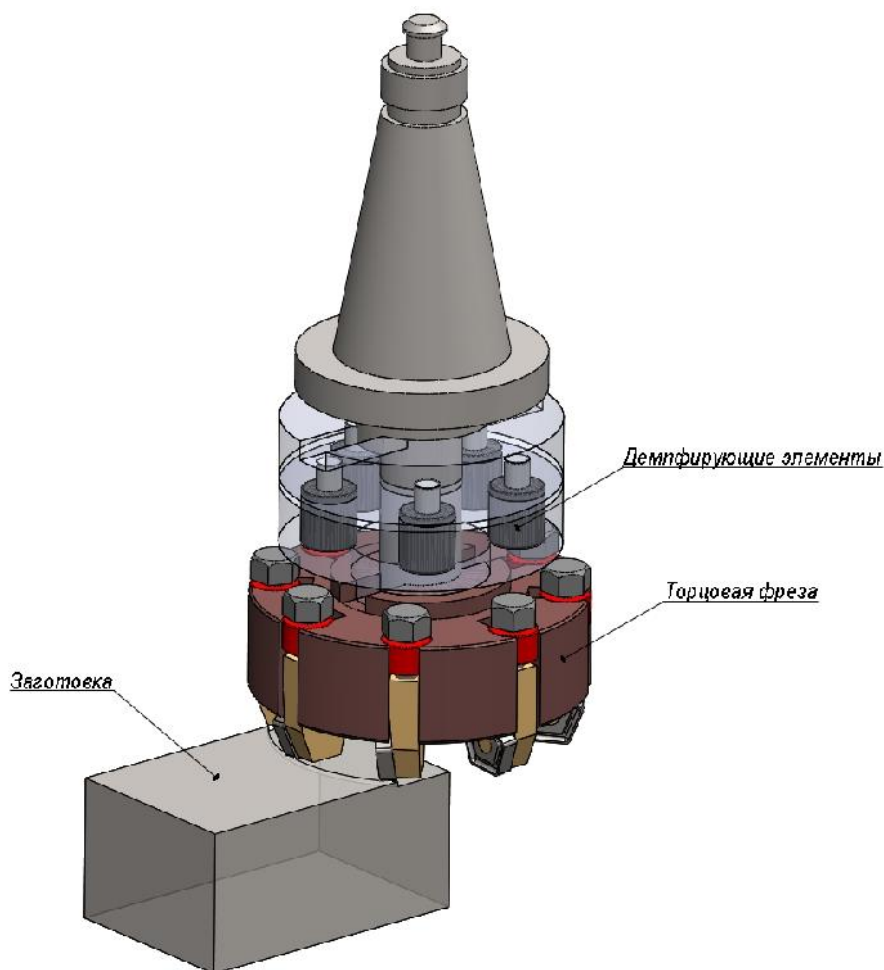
Динамическая модель процесса резания стальной заготовки сборной торцовой фрезой с демпфирующими элементами
